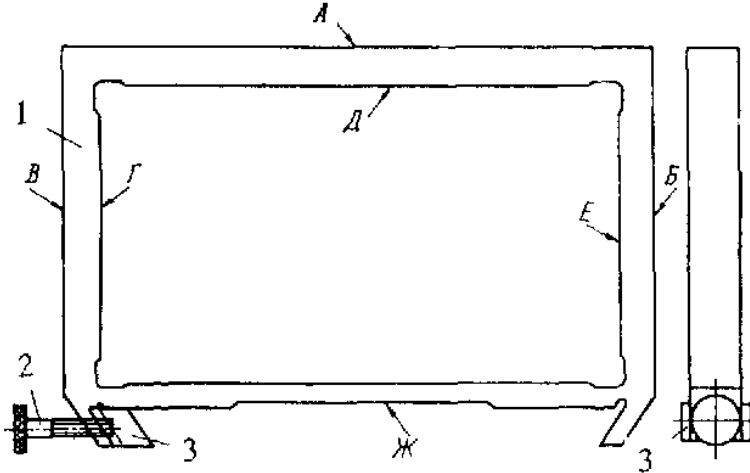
Пристрій для точного установа лещат і заготовок на столі фрезерного верстата
